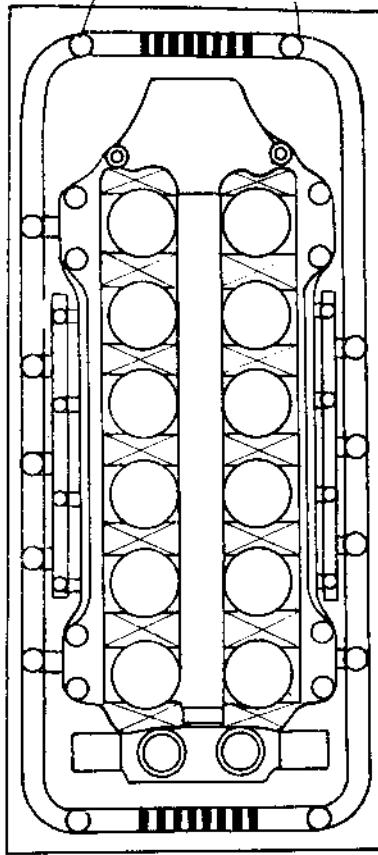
Формовка нижнего картера фланцем вверх, подвод металла рожками вниз.
